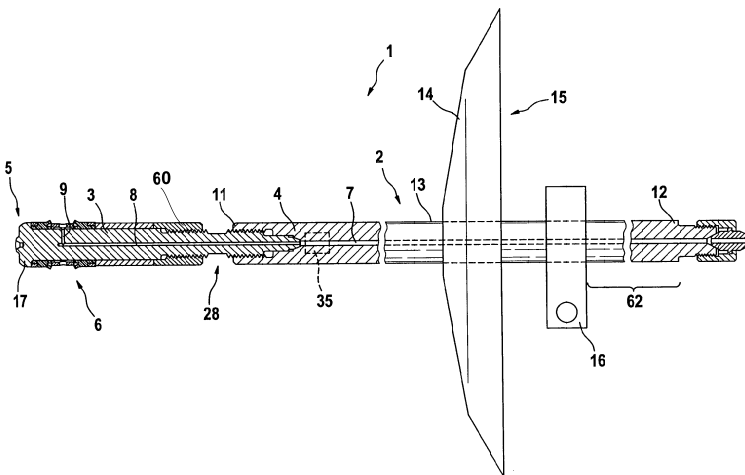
Fügwerkzeug mit einer Fügstelle /2/
